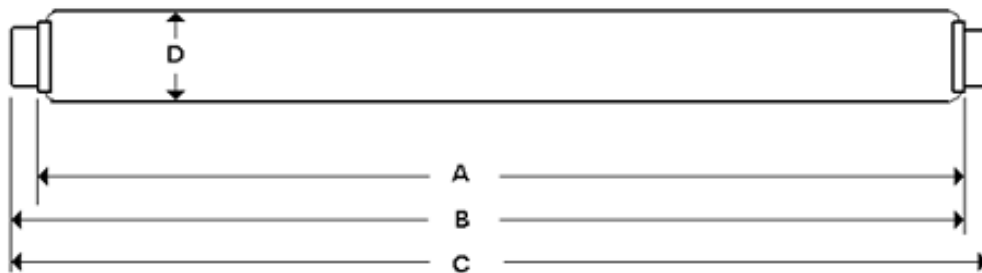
Dimensiones de la lámpara con casquillo R17d
